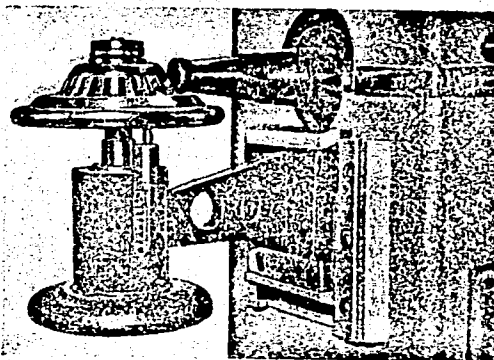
Приспособление для ультразвуковой сварки малых металло-керамических контактов.
